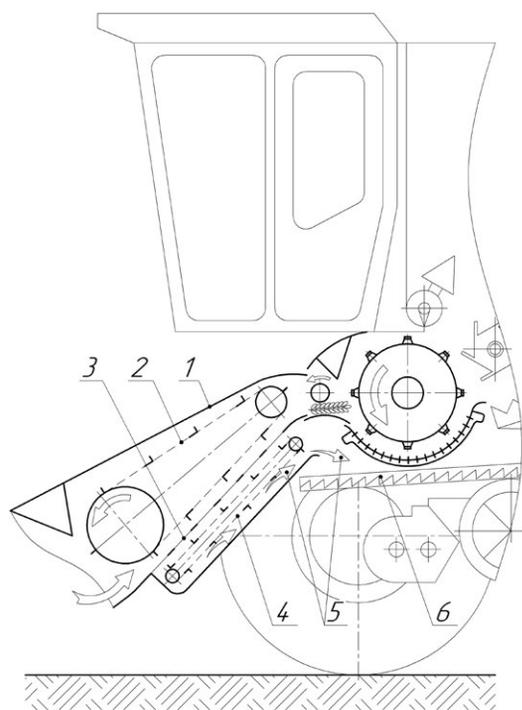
Общий вид зерноуборочного комбайна с модернизированной наклонной камерой: 1 — наклонная камера; 2 — плавающий транспортёр; 3 — решетчатое днище; 4 — дополнительный скребковый транспортёр; 5 — свободное зерно; 6 — транспортная доска.
